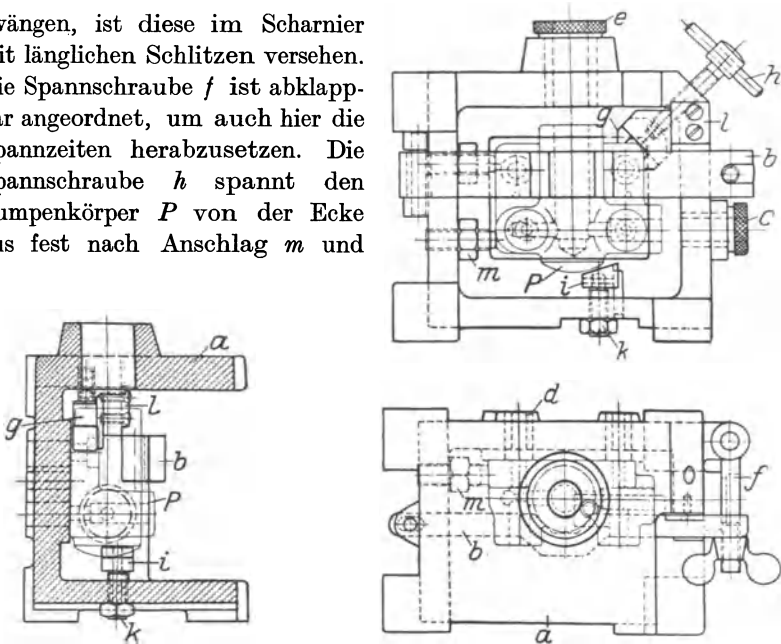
Bohrvorrichtung für Pumpenkörper.
